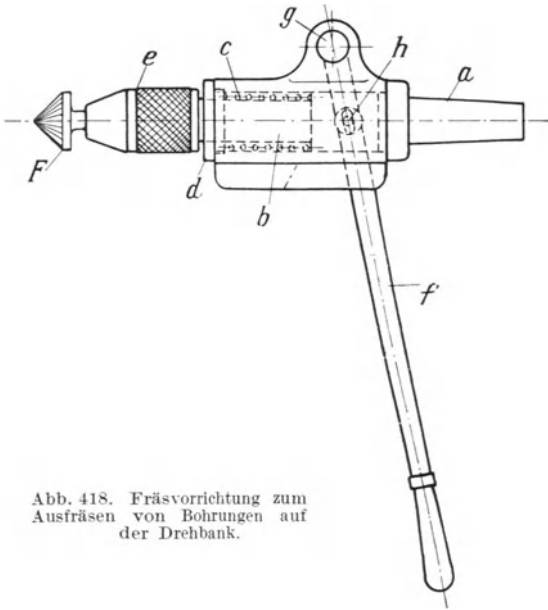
Fräsvorrichtung zum Ausfräsen von Bohrungen auf der Drehbank.
